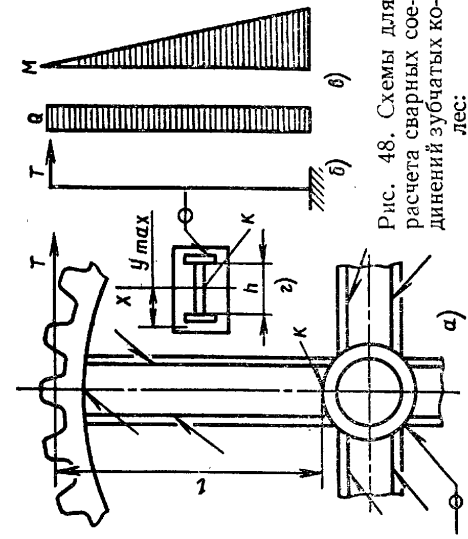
Схемы для расчета сварных соединений зубчатых колес:
